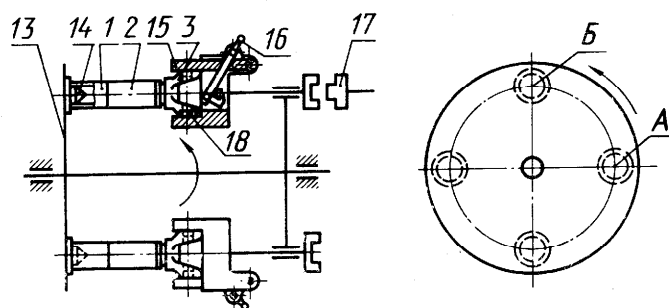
Карданный вал с соединениями, выполненными дуговой сваркой
